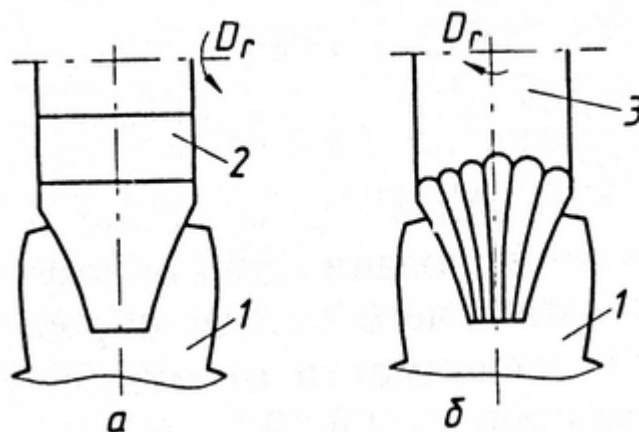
Схемы фрезерования зубчатых колес методом копирования:
